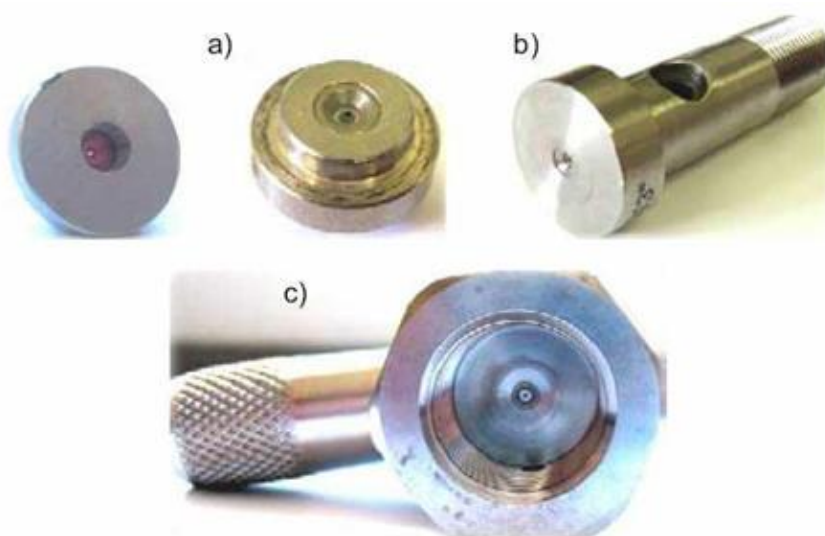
Řezací hlavy pro abrazivní vodní paprsky [31]
